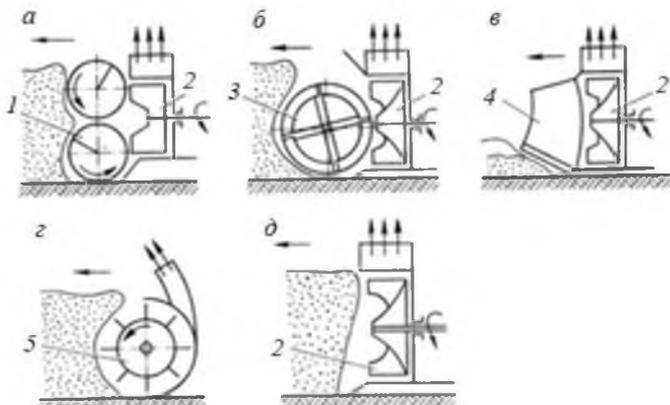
Типы рабочих органов роторных снегоочистителей: *а* – шнеко-роторный; *б* – фрезерно-роторный; *в* – плужно-роторный; *z* – фрезерный; *д* – роторный; 1 – шнек; 2 – ротор; 3 – фреза ленточная; 4 – плуг; 5 – фрезерный барабан. Горизонтальной стрелкой показано направление движения снегоочистителя.
